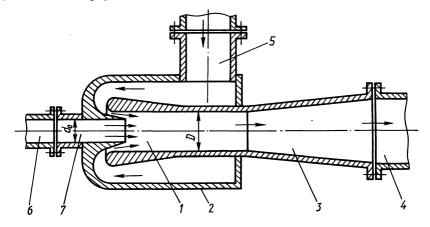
Принципиальная схема струйного рыбонасоса: 1 — камера смешения; 2 — корпус; 3 — диффузор; 4 — канал для транспортирования смеси вода-молодь рыбы; 5 — патрубок; 6 — рыбоотвод; 7 — всасывающий патрубок.
